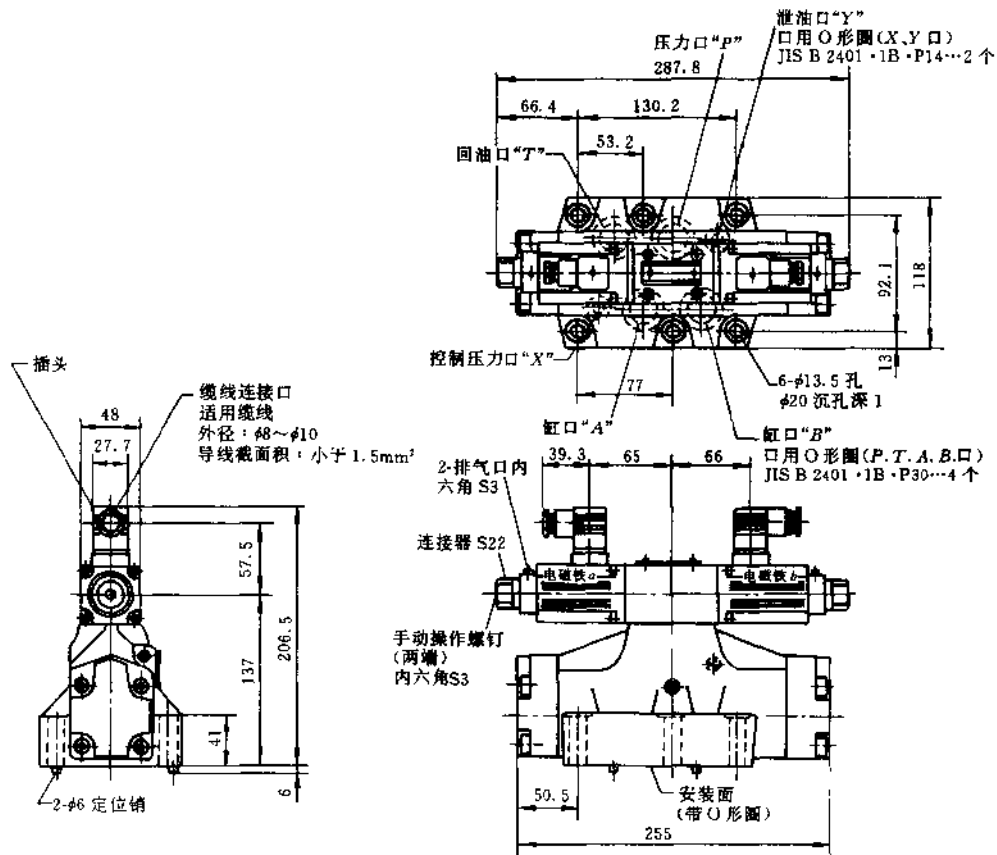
EDFHG-06 型电液比例换向阀外形尺寸
